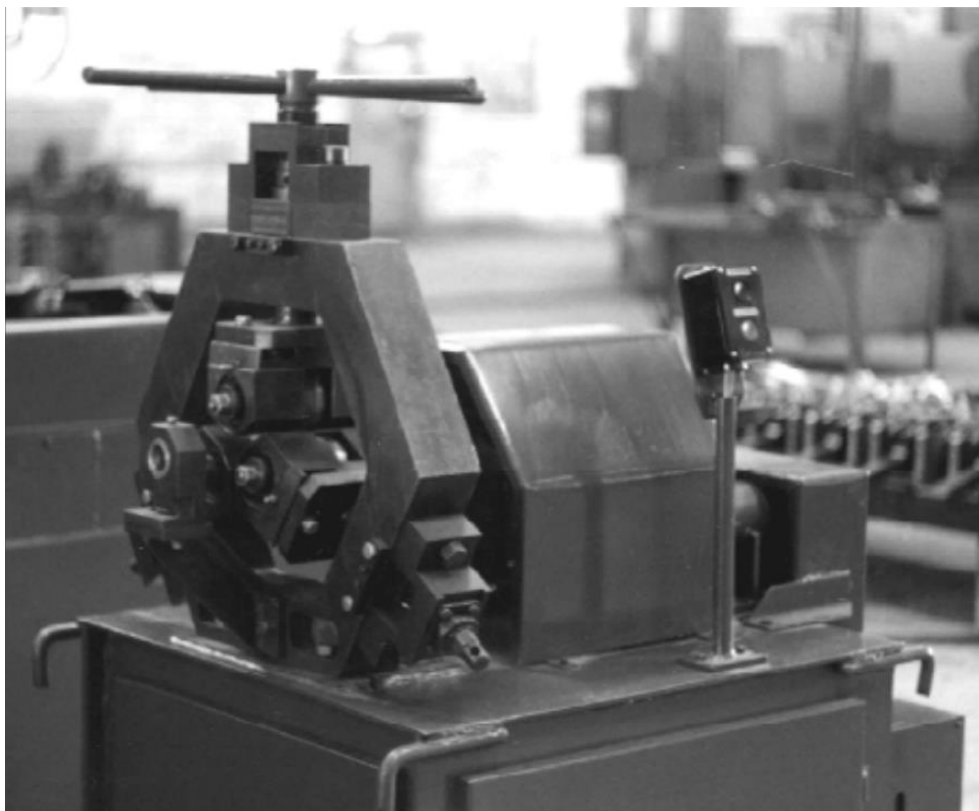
Внешний вид устройства для накатки спиральных канавок [76]
